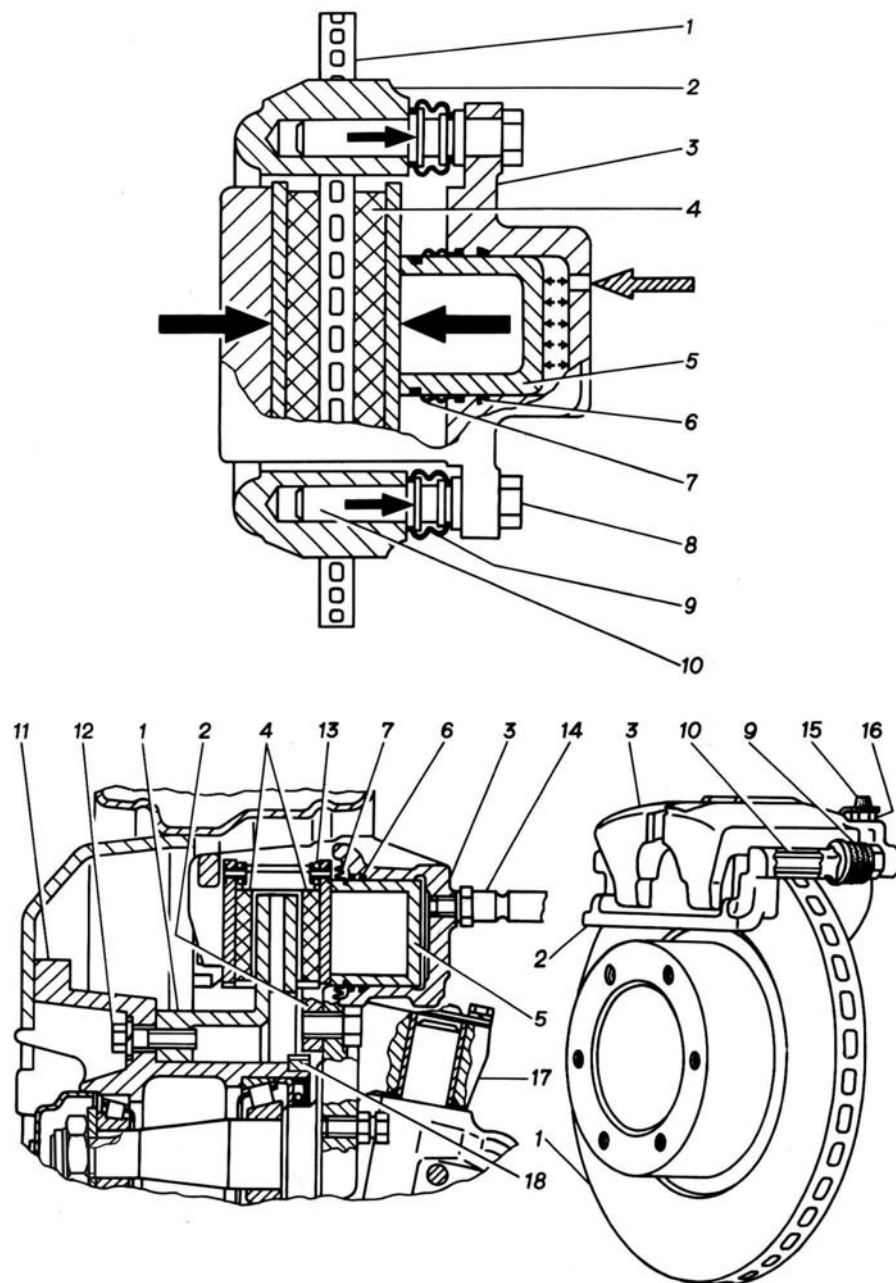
Тормозной механизм передних колес: 1 – тормозной диск; 2 – основание тормозной скобы; 3 – корпус тормозной скобы; 4 – тормозные колодки; 5 – поршень; 6 – уплотнительное кольцо; 7 и 9 – защитные чехлы; 8 и 12 – болты; 10 – направляющий палец; 11 – ступица колеса; 13 – пружина колодки; 14 – шланг подвода тормозной жидкости; 15 – колпачок; 16 – клапан прокачки; 17 – поворотный кулак; 18 – ротор АБС (для автомобилей с АБС)
